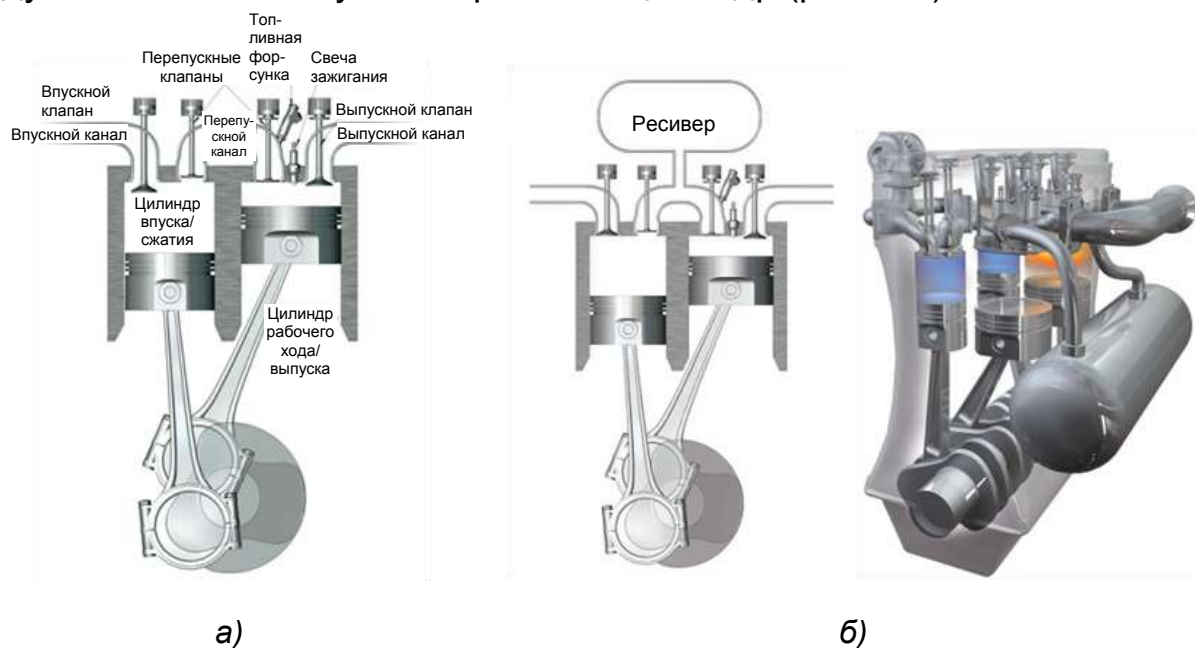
Двигатель Скудери: а) схема двигателя; б) двигатель с ресивером
